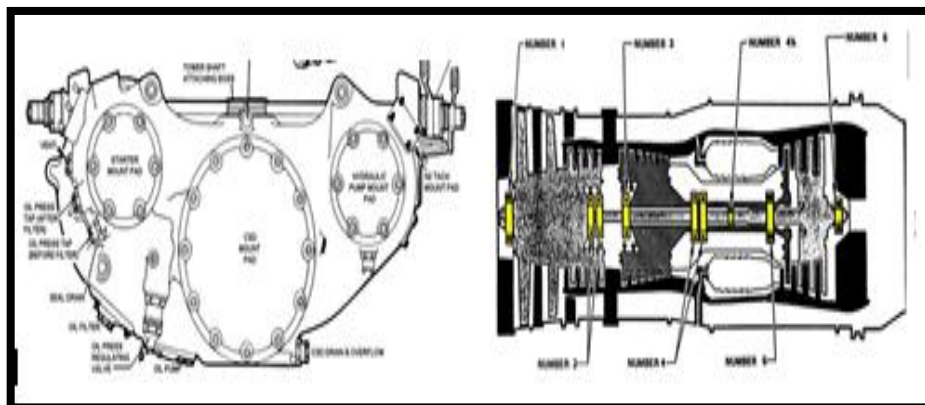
Lubricación de los cojinetes y de la caja de engranajes
